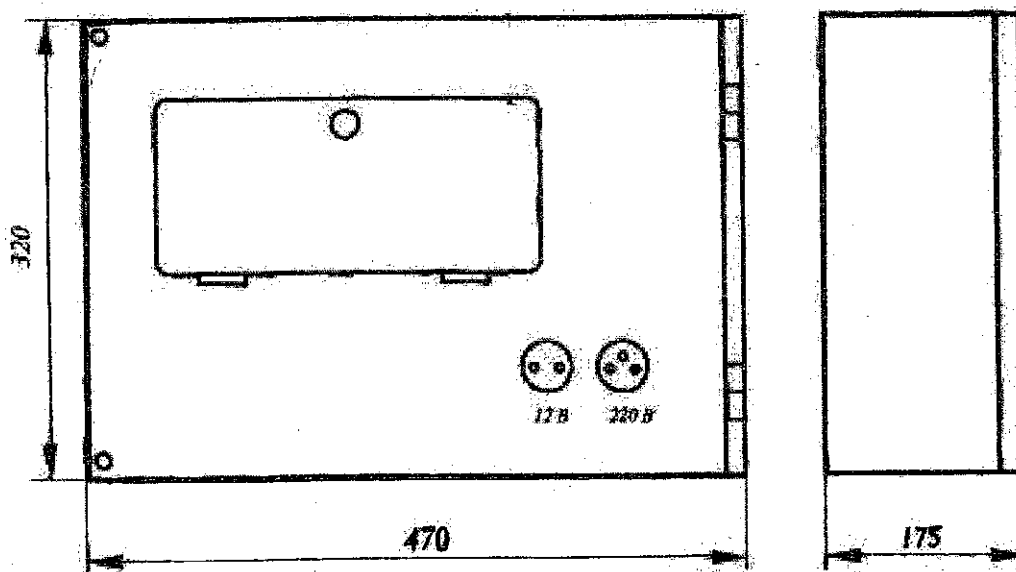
Габаритные размеры щитка гаражного ЯВУ-1Г-40-УХЛ4
